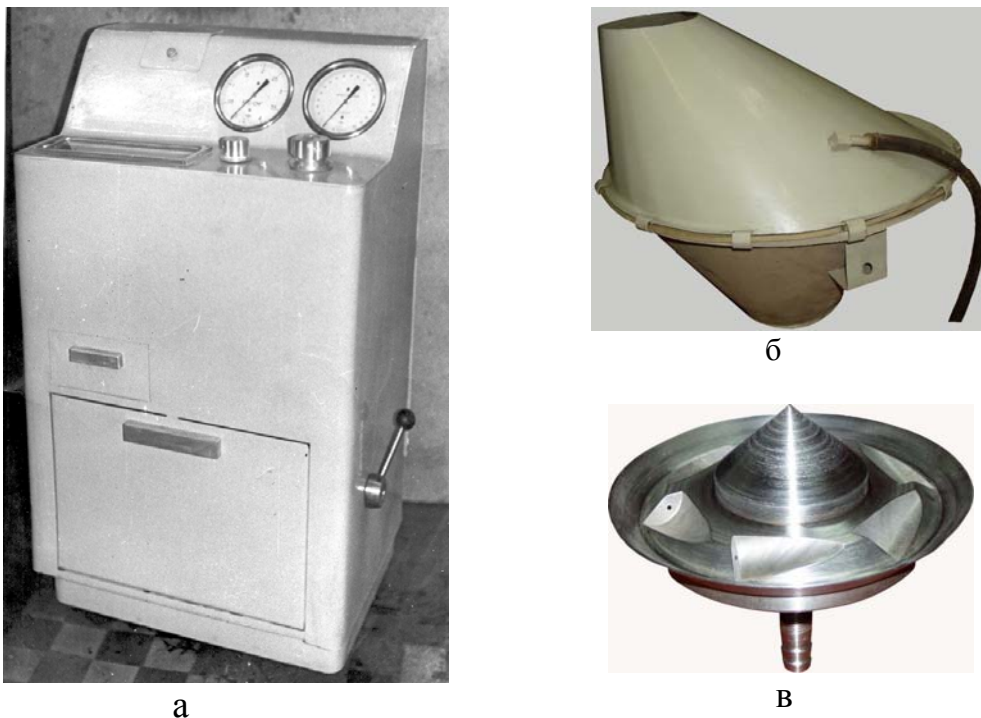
Установа для абразивної обробки деталей затопленими струменями (а) та її складові: робоча камера (б), сопловий апарат (завихрювач) (в)
